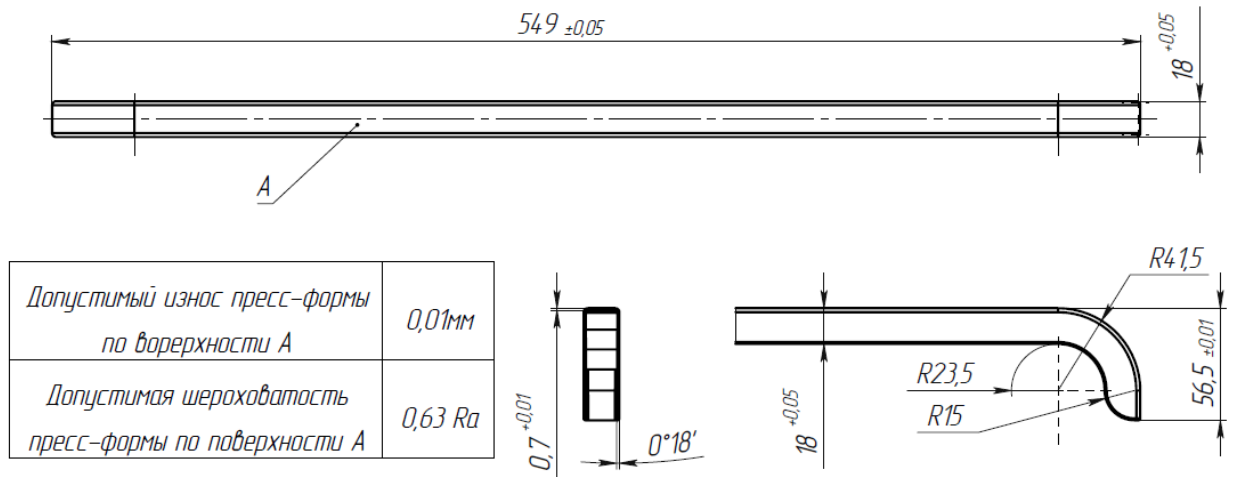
Эскиз литейной детали из ПКМ «Накладка»
